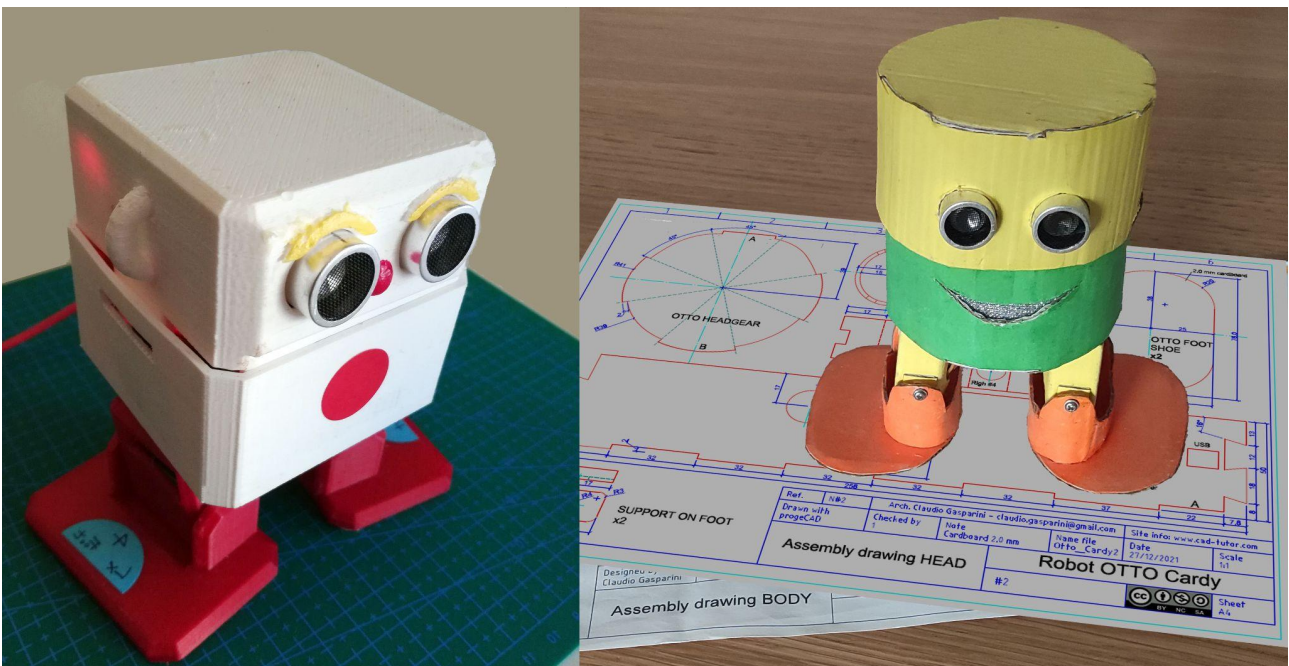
A sinistra OttoDIY realizzato con la stampante 3D e a destra la versione di cartone OttoCardy con i due disegni tecnici forniti per la sua costruzione
